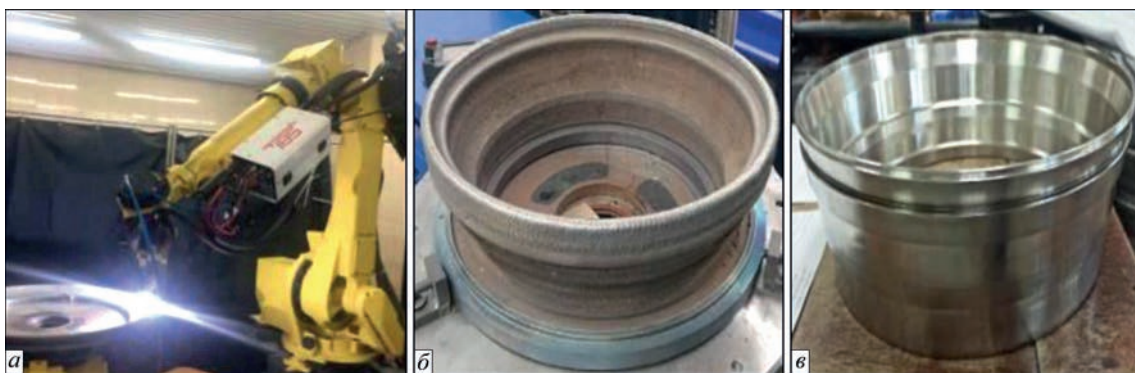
Процес АПДН (3D друку) заготовки із нікелевого жароміцного сплаву EI 868 (ХН60ВТ) (а), заготовка деталі після 3D друку (б), готова деталь після механічної обробки (в) [14]
